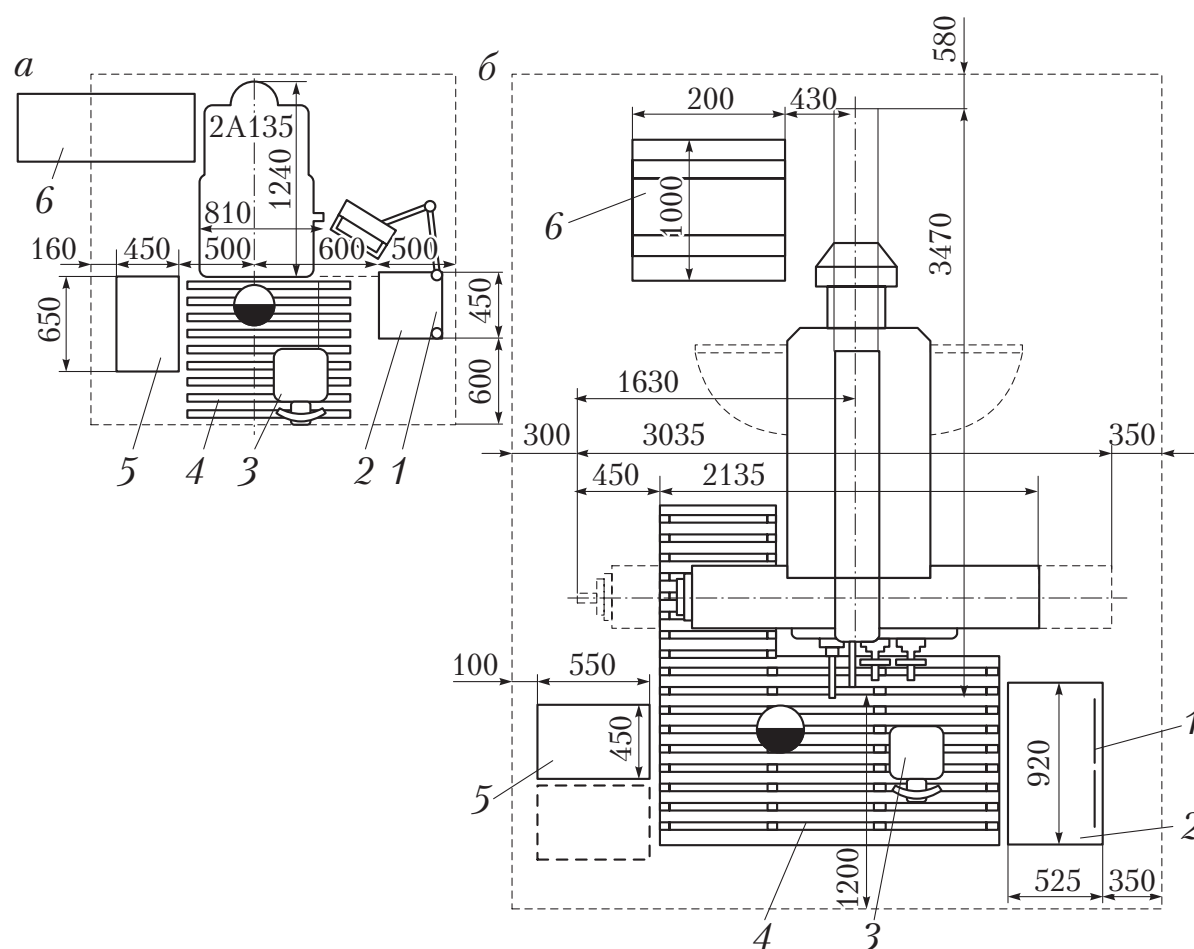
Планировка рабочих мест сверловщика (а) и фрезеровщика (б):
